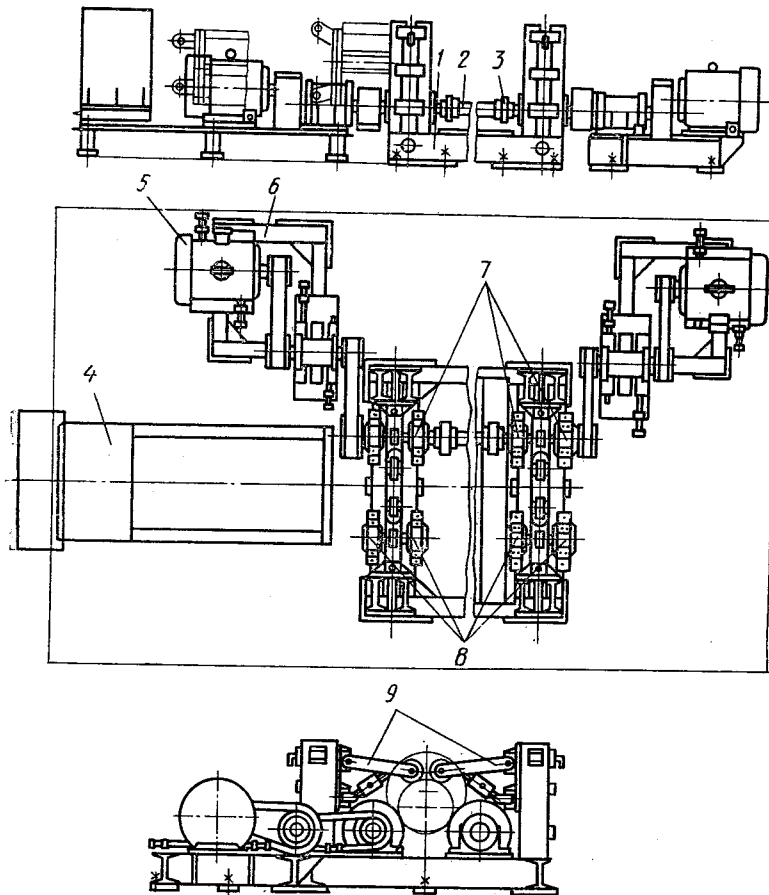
Роликовая центрифуга СМЖ-169А для формования опор:
